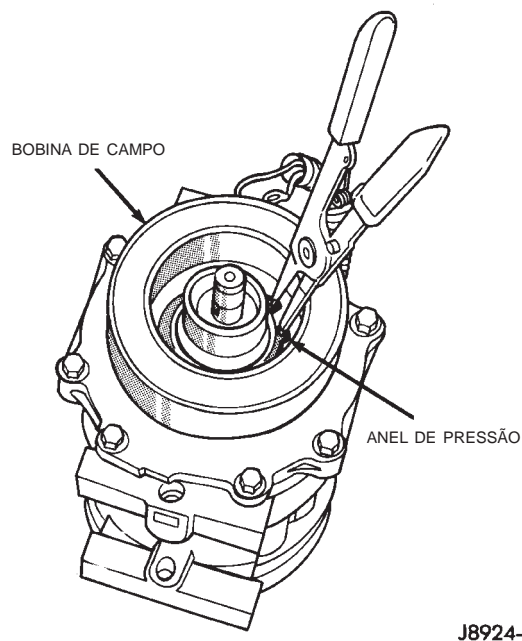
Remoção do Anel de Pressão da Bobina de Campo do Acoplador
